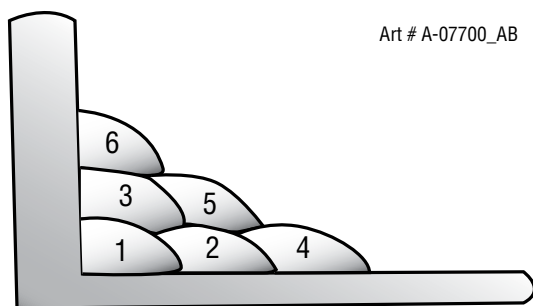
Plusieurs cordons dans la soudure du joint HV
